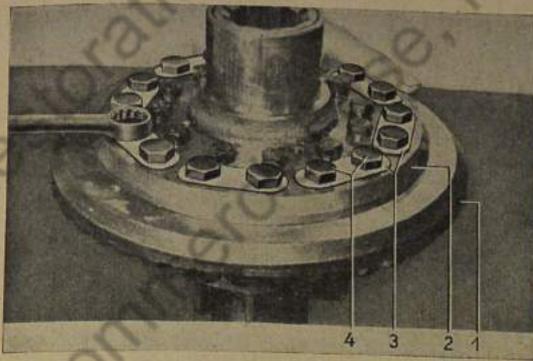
Tellerrad vom Ausgleichgehäuse abschrauben
